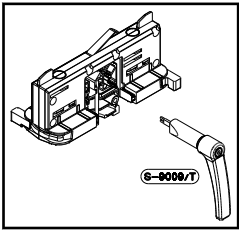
Cablaggio dell'adattatore - Pic.1 Adapter wiring
